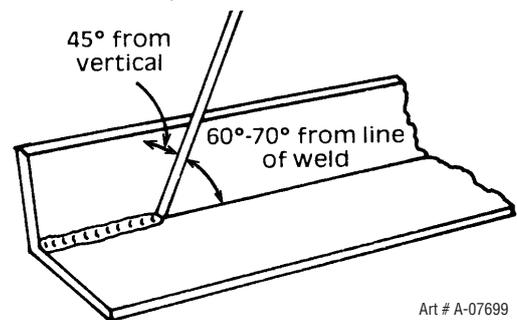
Position de l'électrode pour la soudure du joint HV
